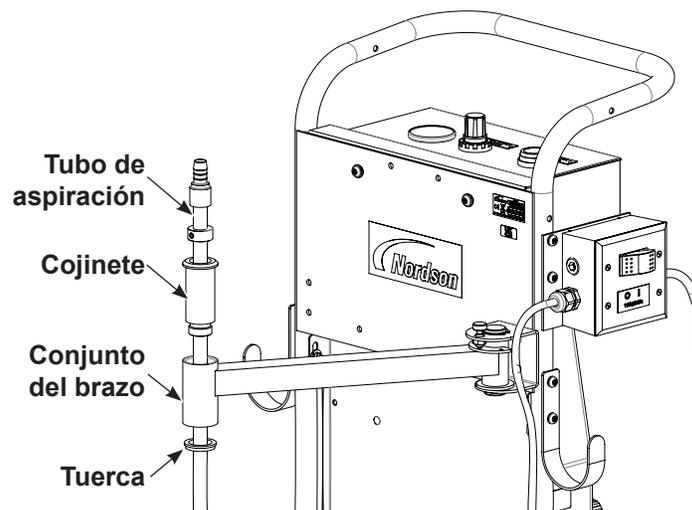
Instalar el conjunto de tubo de aspiración en el conjunto del brazo
